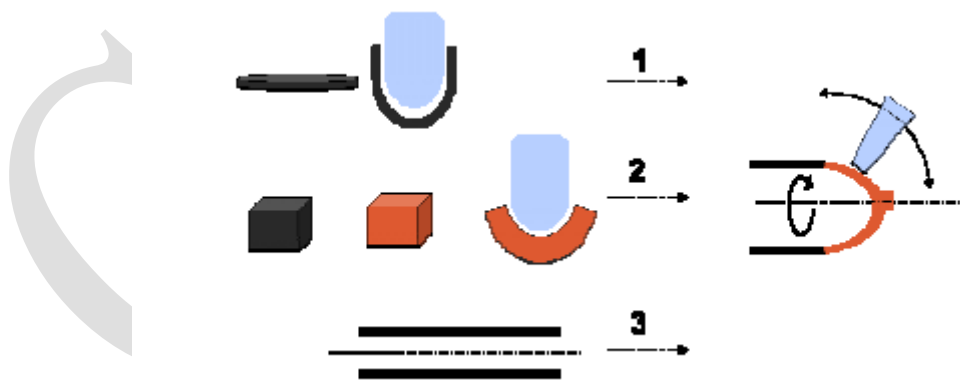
Принцип процесів виготовлення металевих резервуарів
